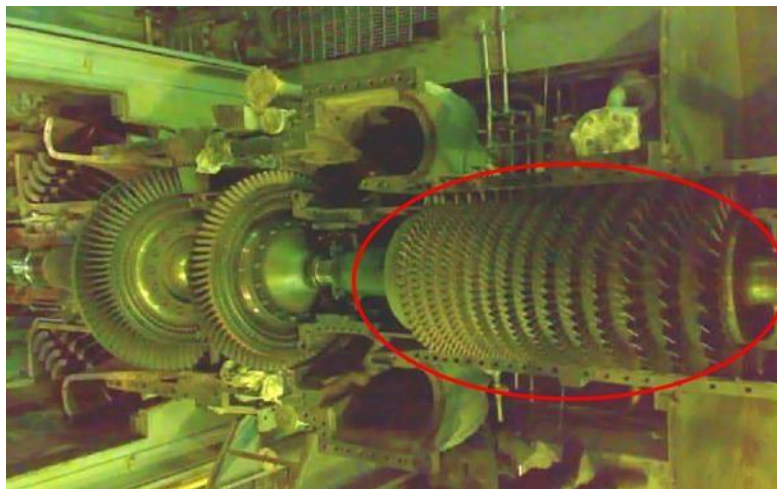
Compresseur axial d'une turbine MS 3002J
